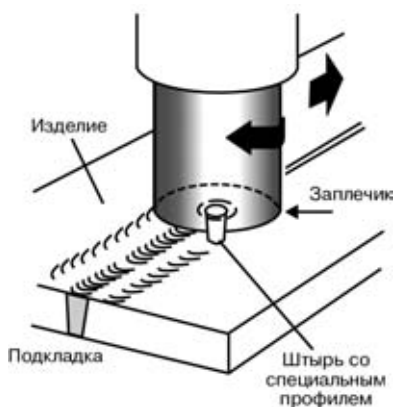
Схема процесса сварки трением с перемешиванием
